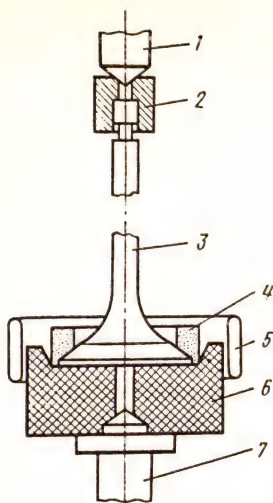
Схема установки клапана при индукционной наплавке рабочей фаски головки высокой частоты:
